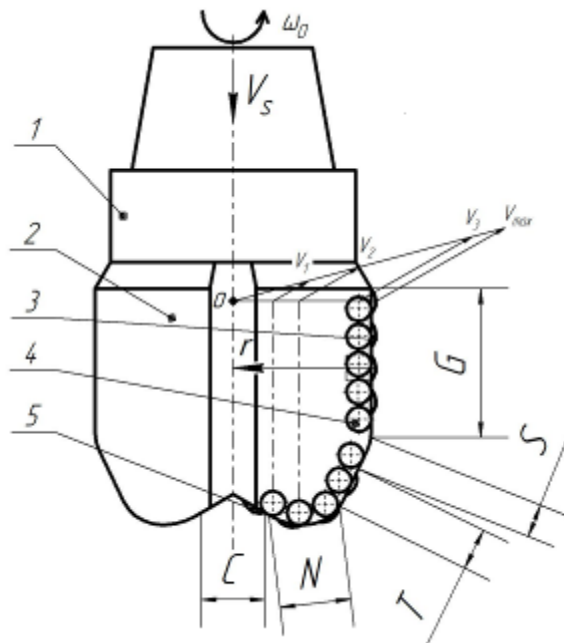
Кинематика и характерные поверхности долот со вставками из искусственных сверхтвердых материалов (ИСМ): 1- корпус; 2-лопасть; 3-калибрующий резец; 4-скалывающий резец; 5-дробящий резец; С-внутренняя конусная поверхность; N-торцовая режущая поверхность; Т-наружная конусная поверхность; S- поверхность сопряжения; G- калибрующая поверхность; V_1, V_2, V_3, V_{max} - окружные скорости резания; r- радиус долота; ω - частота вращения; V_s -скорость подачи; ω_D -частота вращения долота.
